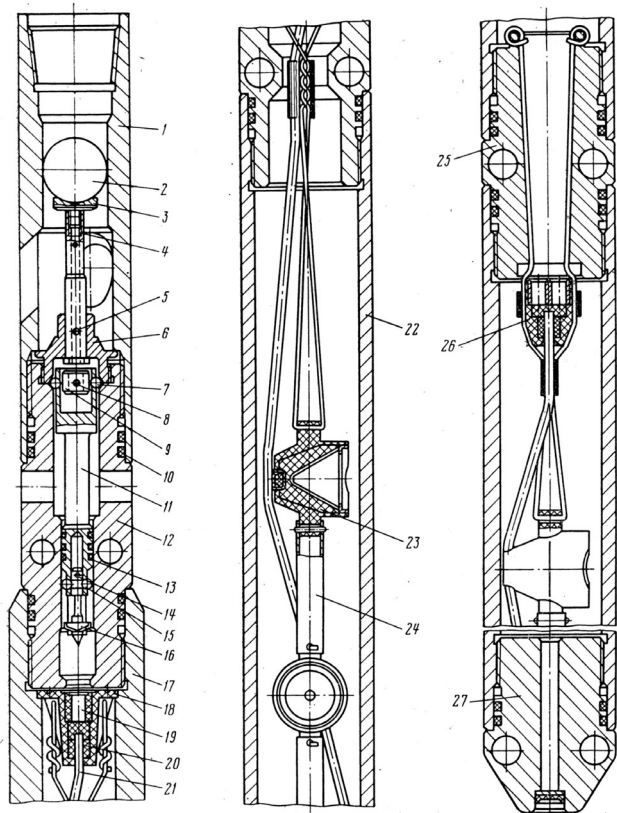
Устройство перфоратора ПНКТ-89: 1 – муфта-переходник к колонне насосно-компрессорных труб; 2 – резиновый шар; 3 – упор штока; 4 – шток; 5, 8, 14 – чека; 6 – стопорная гайка; 7, 15 – предохранительные шарики; 9 – втулка; 10, 13 – резиновые уплотнительные кольца; 11 – ударник; 12 – корпус взрывного устройства; 16 – боек; 17 – корпус головки перфоратора; 18 – пластмассовый корпус инициирующего устройства; 19 – капсюль-детонатор; 20 – шашки ВВ; 21 – детонирующий шнур; 22 – корпус перфоратора; 23 –кумулятивные заряды; 24 – соединительная втулка; 25 – переходник; 26 – устройство передачи детонации; 27 – наконечник
